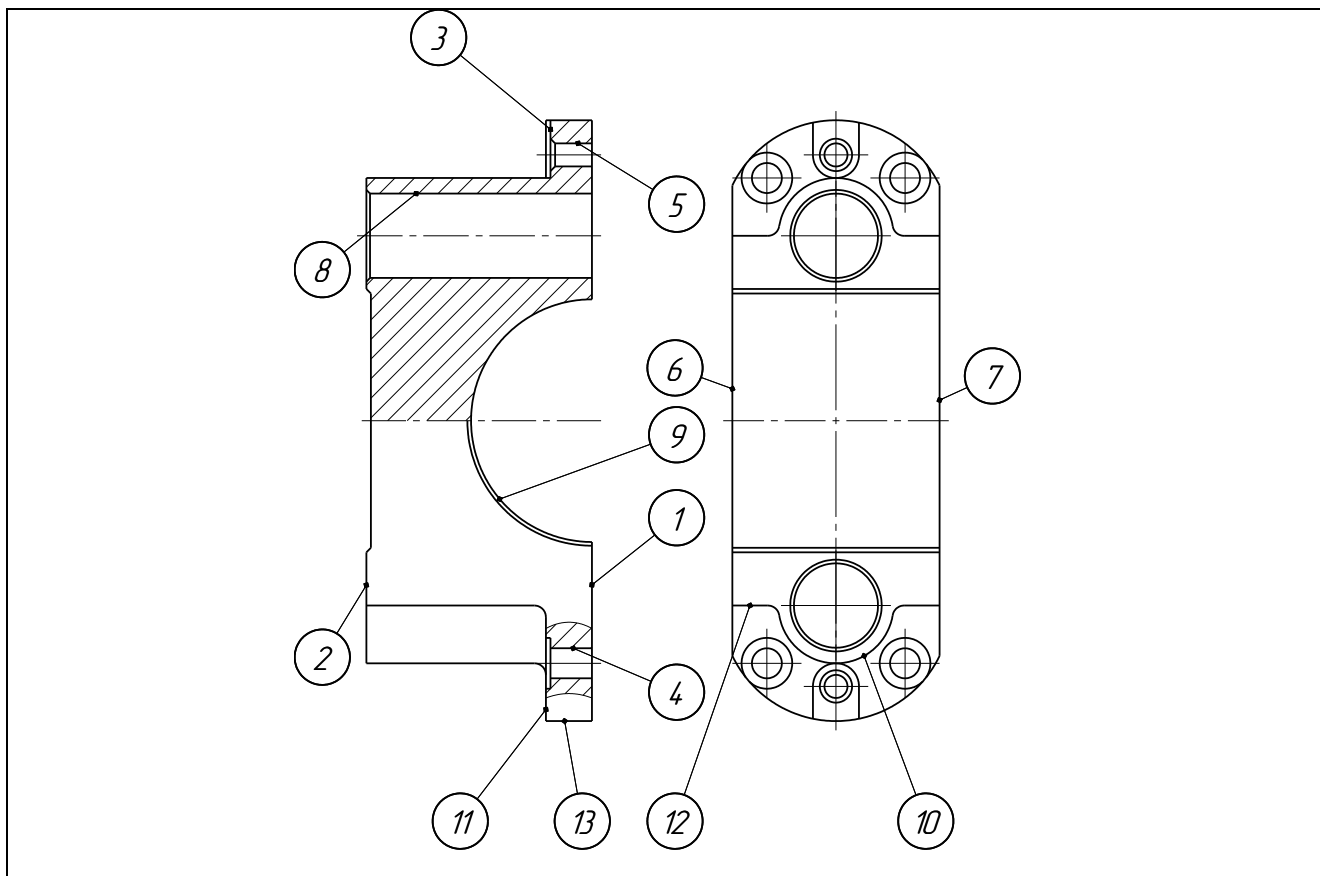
Нумерація поверхонь деталі корпус
